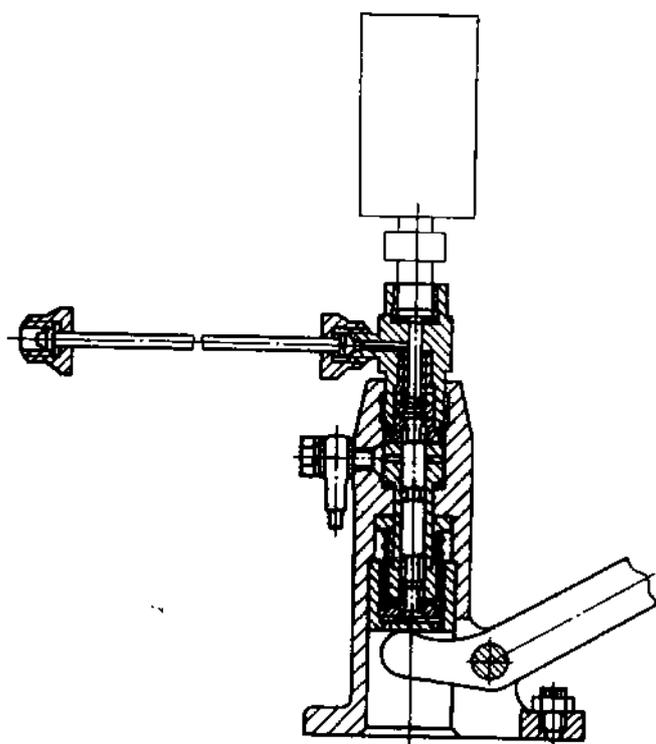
Приспособление для проверки работы форсунок 01-8733 /ручной топливопрокачивающий насос/
